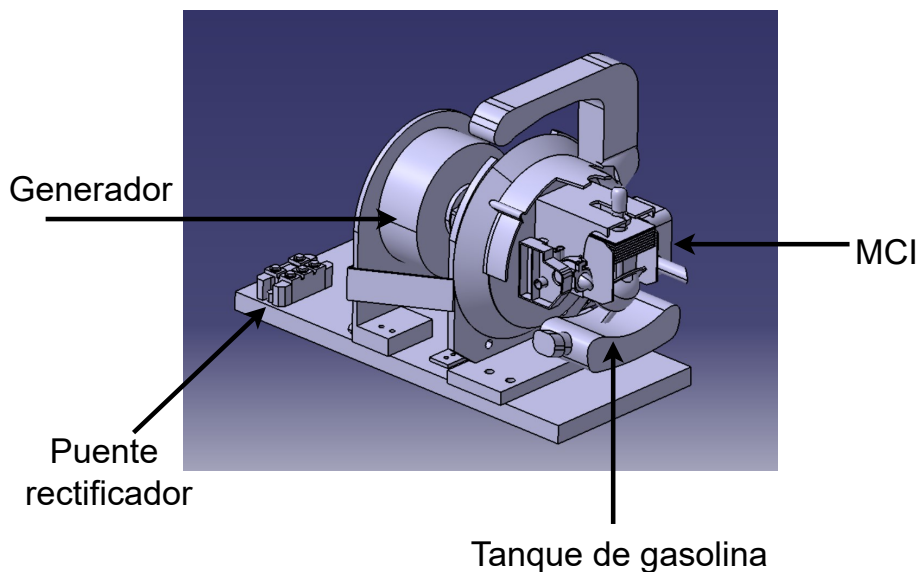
Vista isométrica del diseño en CAD del sistema físico.
